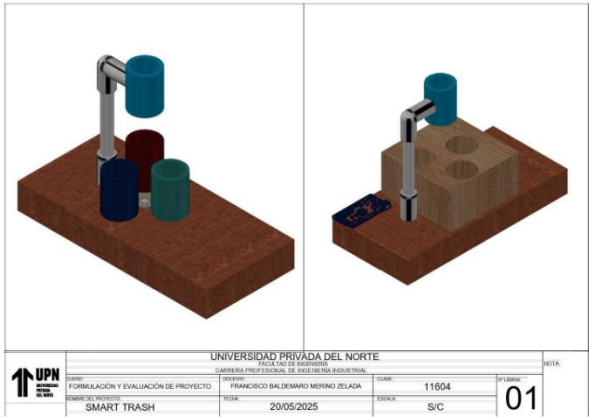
Planos de desarrollo de Proyecto (AutoCAD)
